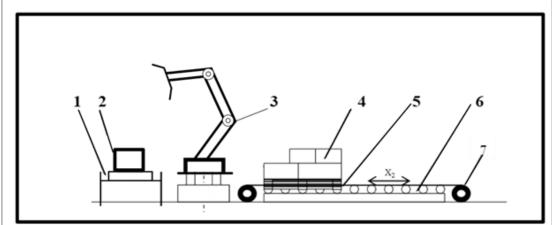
Напольный пакетоформирующий автомат с манипулятором: 1 – конвейер подачи коробок с грузом; 2 – коробки с грузом; 3 – перегрузочный манипулятор с автоматическим распознаванием QR-кода; 4 - формируемый транспортный пакет; 5 – плоский деревянный поддон; 6 – конвейер для транспортировки готовых пакетов; 7 – управляемый электропривод конвейера.
